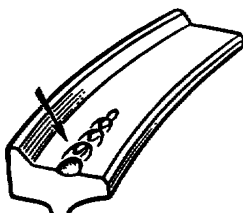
Смещение металла ("навар") на поверхности катания колеса
